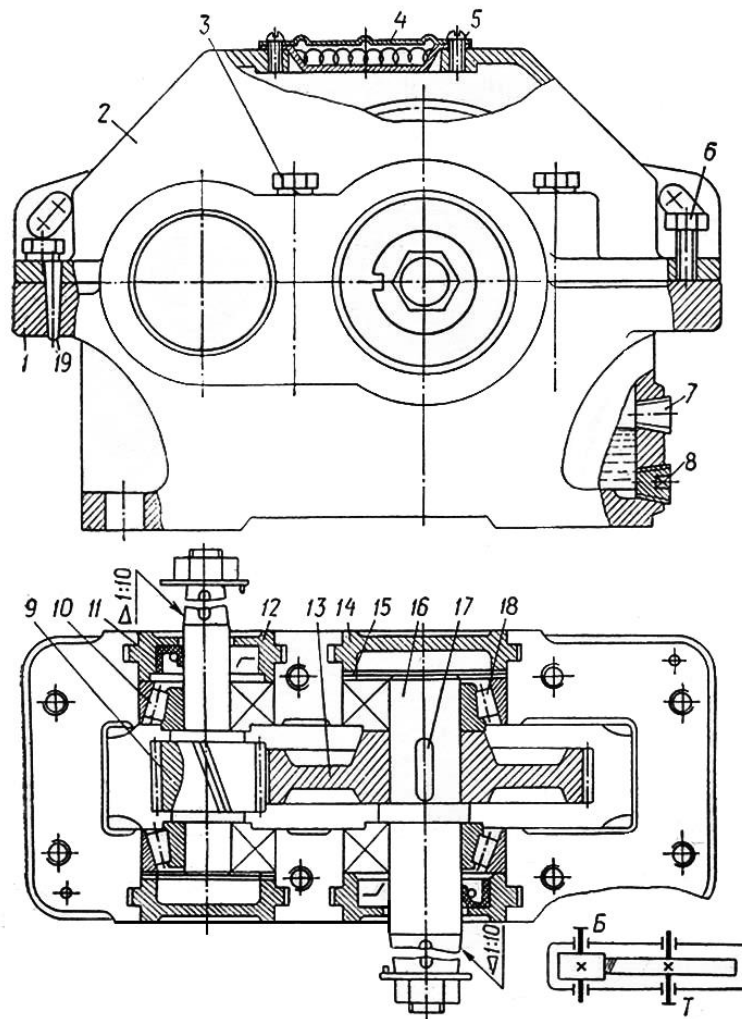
Циліндричний одноступінчастий редуктор
